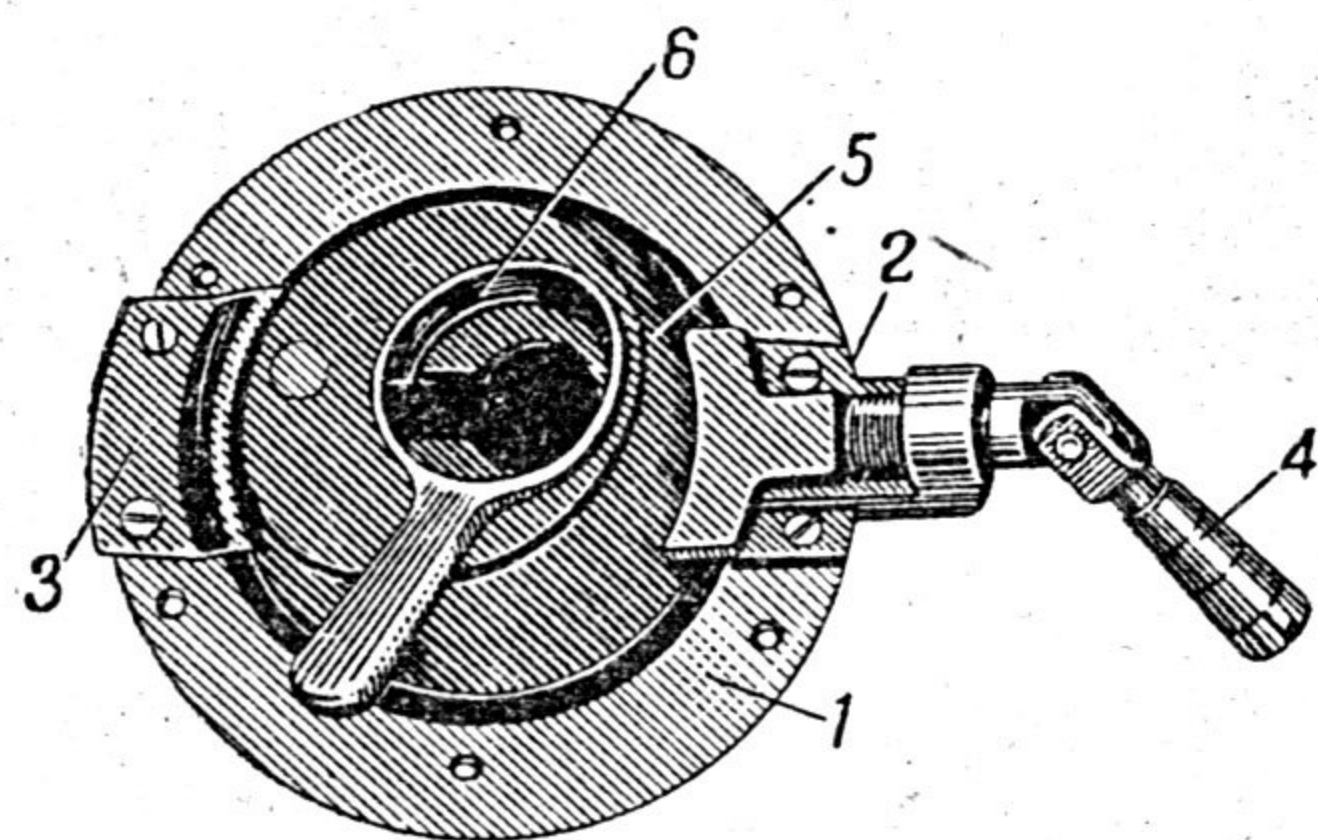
Общий вид шаровой установки пулемета ДТ:
